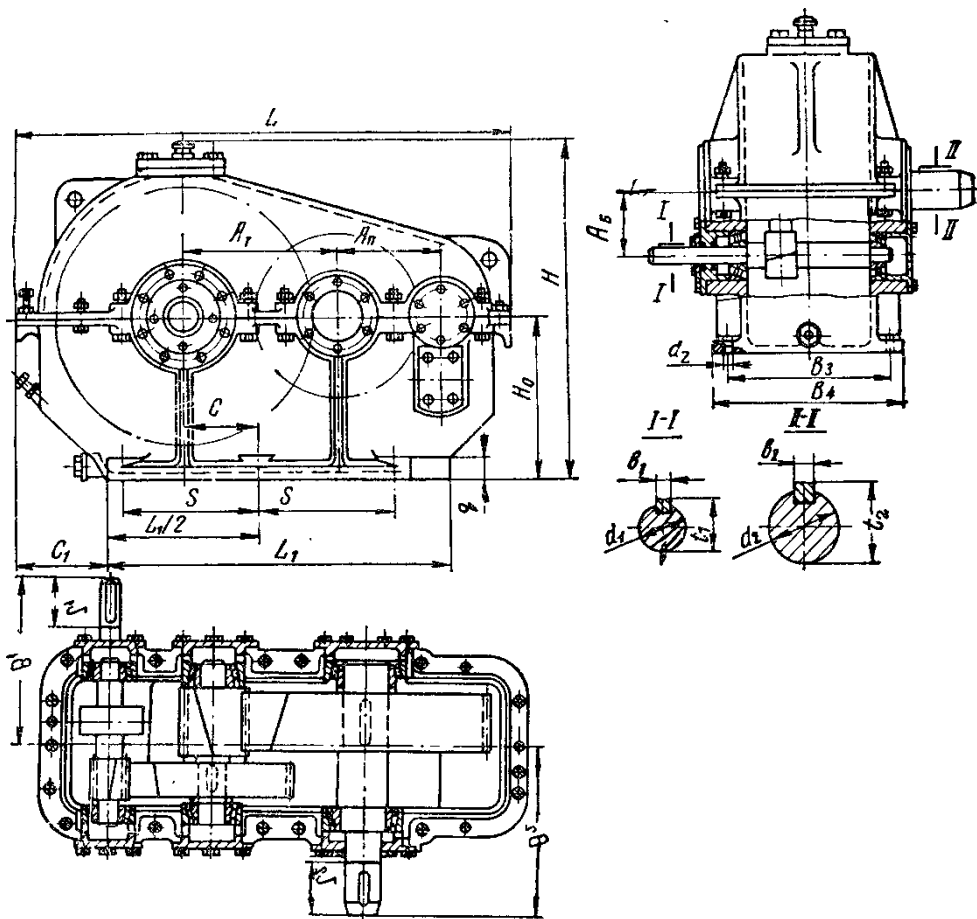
цилиндрический горизонтальный трехступенчатый редуктор типа ГТ-ВК
